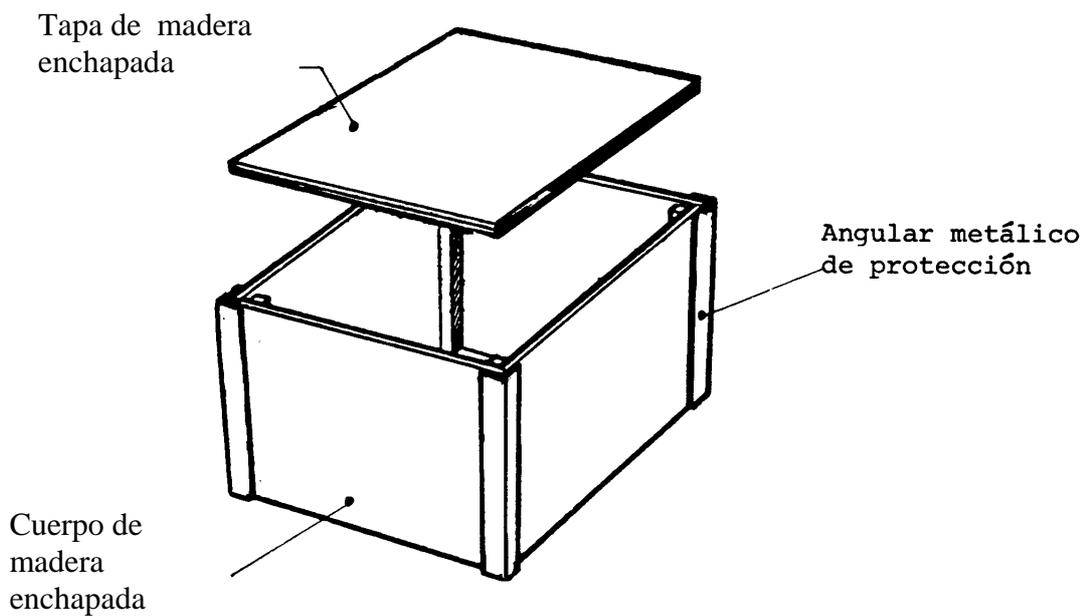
b) - Caja de madera enchapada, con angulares metálicos de protección
